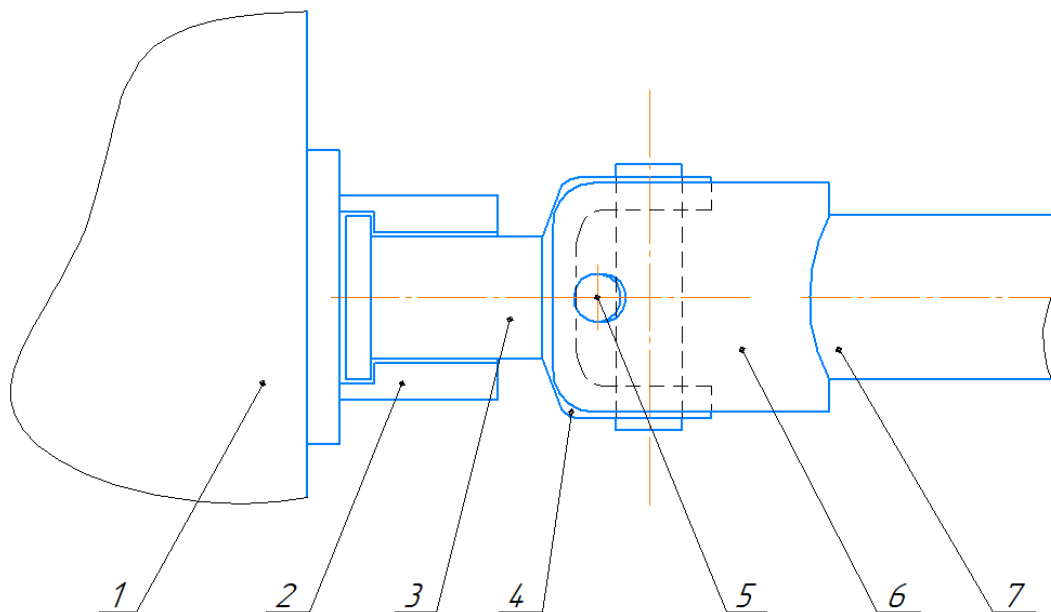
Схема стабілізуючого тягово-зчіпного пристрою (вид зверху): 1 – силовий елемент кузова автомобіля; 2 – кріплення; 3 – шток; 4 – передня вилка; 5 - хрестовина; 6 - задня вилка; 7 - дишло причепа
